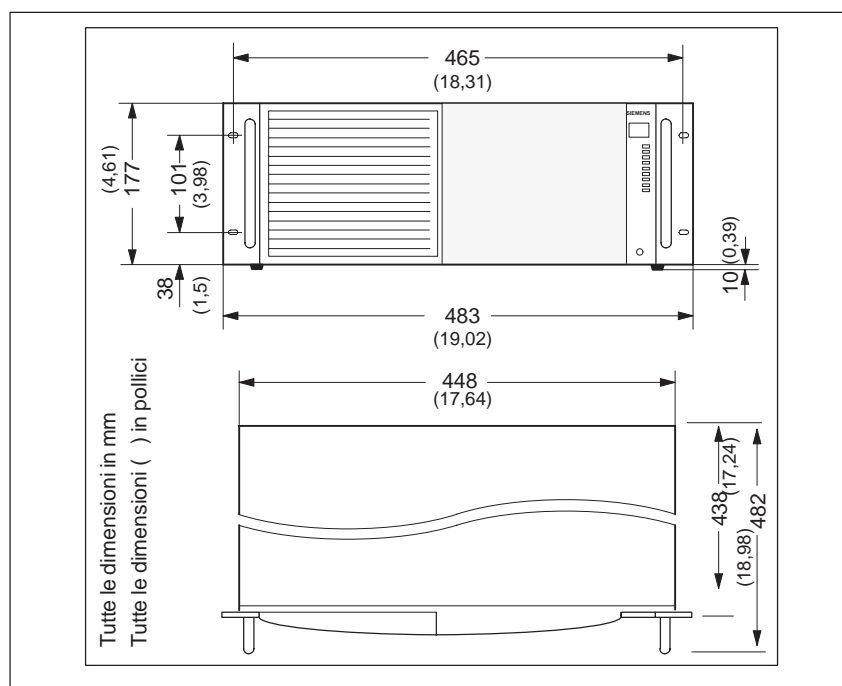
Dimensioni di montaggio del SIMATIC PC RI45 PII
